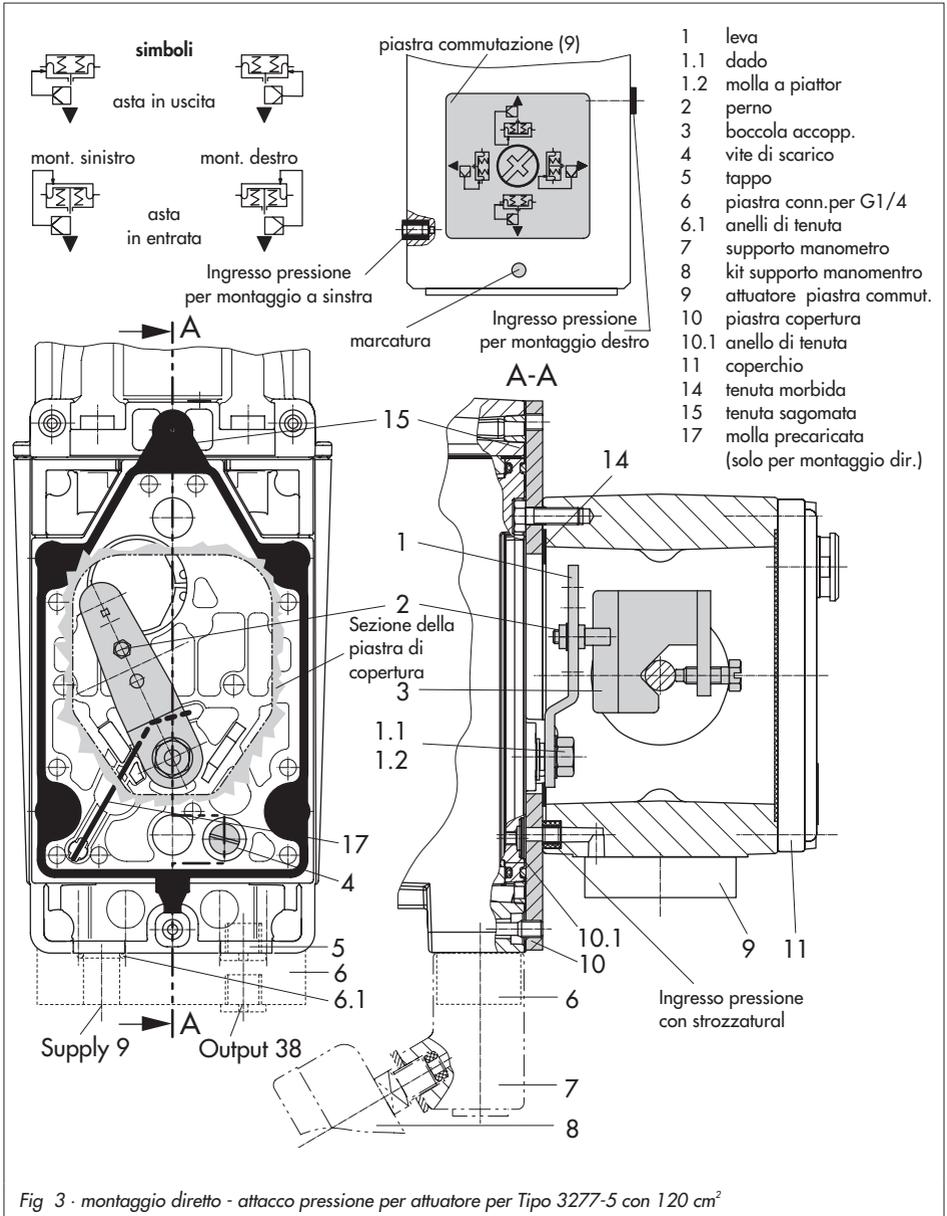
montaggio diretto - attacco pressione per attuatore per Tipo 3277-5 con 120 cm<sup>2</sup>
